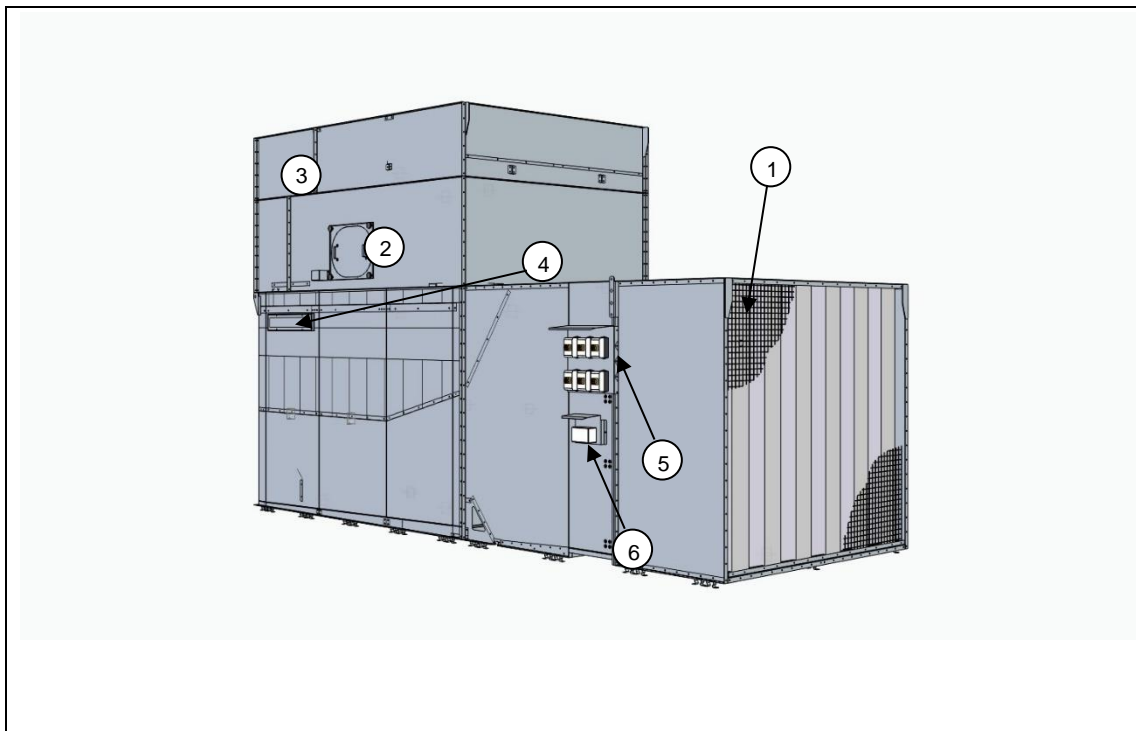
Kühlturm mit Schalldämpfer – seitlich ansaugend – oben ausblasend
